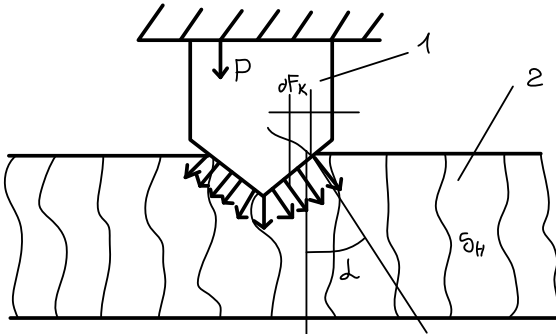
Схема для определения деформирующего усилия: 1-диск круглой формы, конусной поверхности; 2-заготовка древесины.
